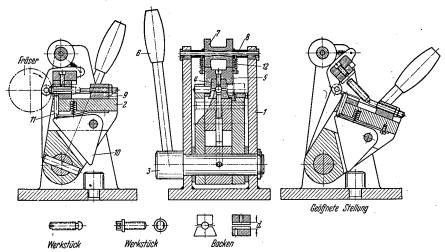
Vorrichtung zum Fräsen von Schlitzen und Schlüsselflächen an Schrauben.
